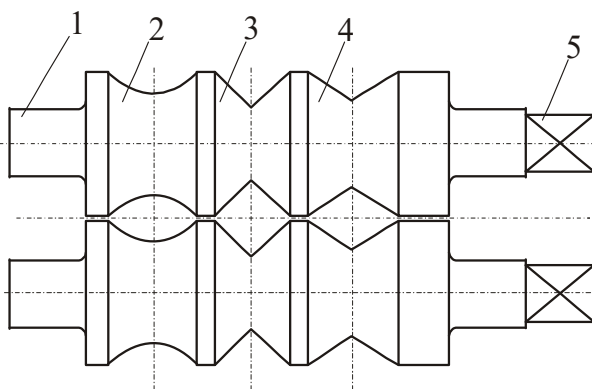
Валки сортового стана : 1 - шийка; 2-4 - калібри; 5 – хвостовик
